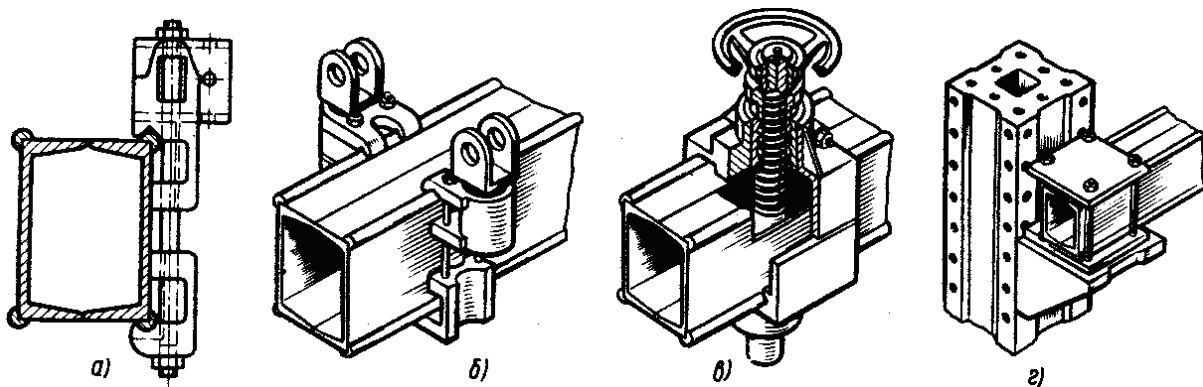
Узлы сборочной оснастки в самолетостроении: а) схема крепления узла на балке ступеля; б) крепление вертикальных вилок; в) выдвижной винтовой фиксатор; г) крепление продольной балки на вертикальной колонне.
